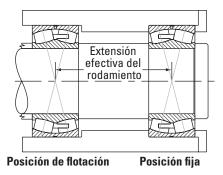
Montaje directo del rodamiento de rodillos esféricos.
